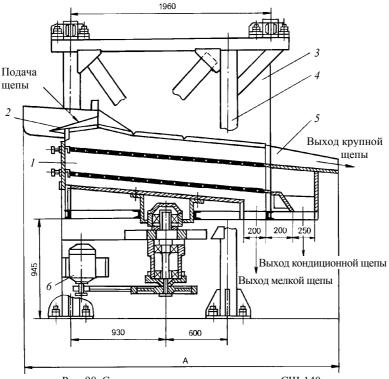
Сортировочная установка для щепы СЩ-140: I – ситовая коробка; 2 – распределитель; 3 – цепная подвеска; 4 – опора; 5 – лоток; 6 – электродвигатель
